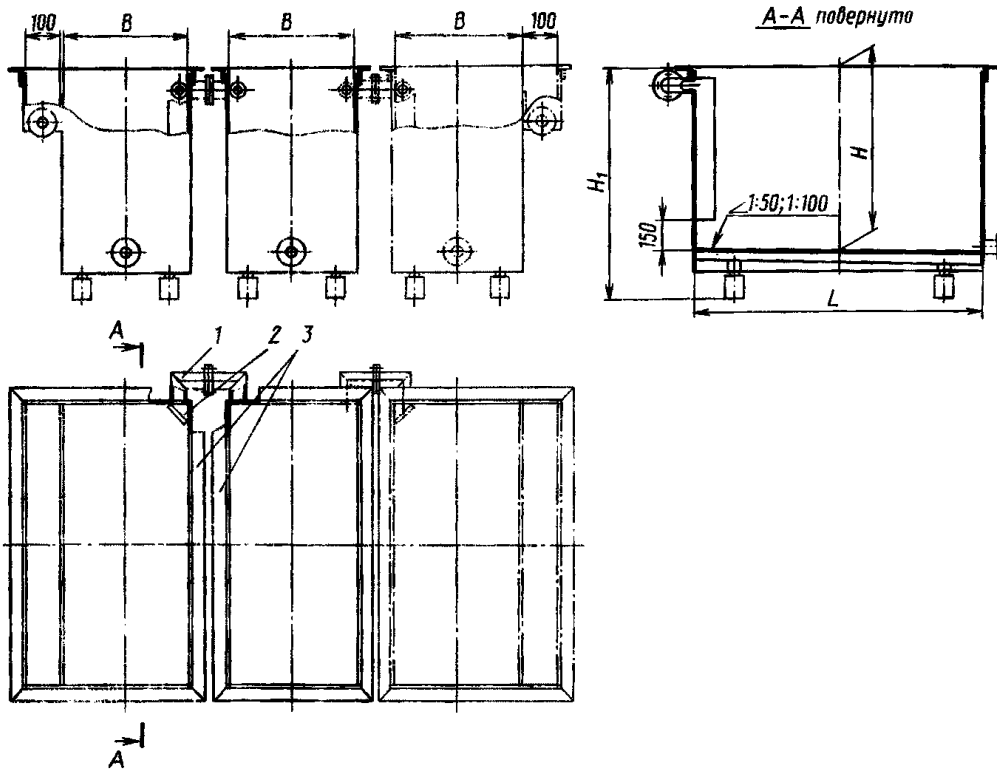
Корпус сборной ванны двухступенчатой противоточной промывки холодной водой.
